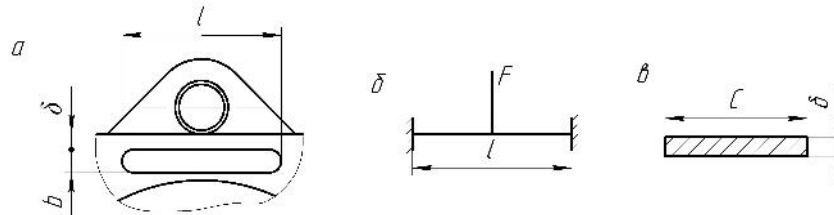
Схеми пружної ділянки: а - конструктивна; б – розрахункова; в – поперечний переріз пружної ділянки
